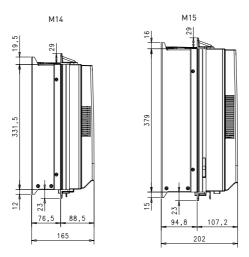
Dimensiones de fondo del montaje con bridas para MI4 y MI5 (Unidad: mm)
